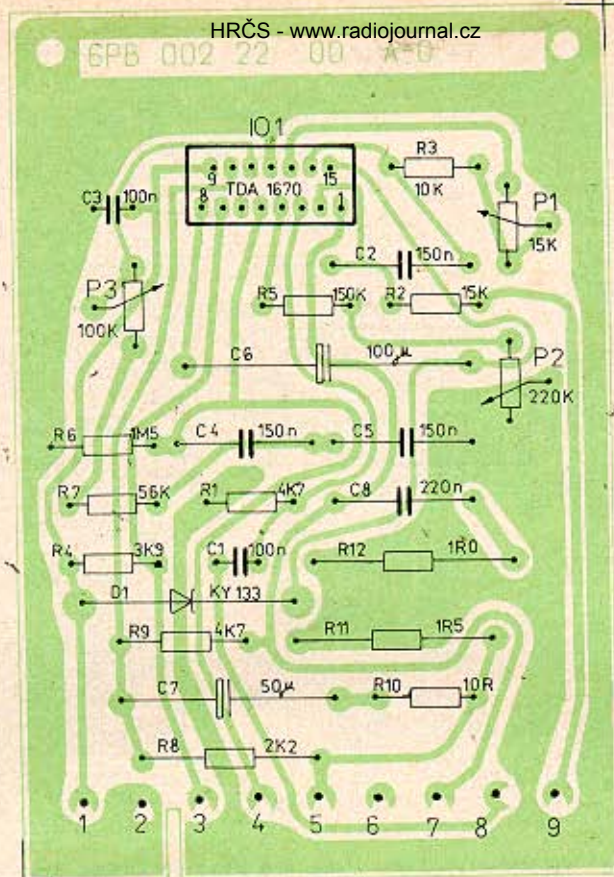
MODUL "P" 6PW 051 006 - POHLAD ZO STRANY SÚČIASTOK
